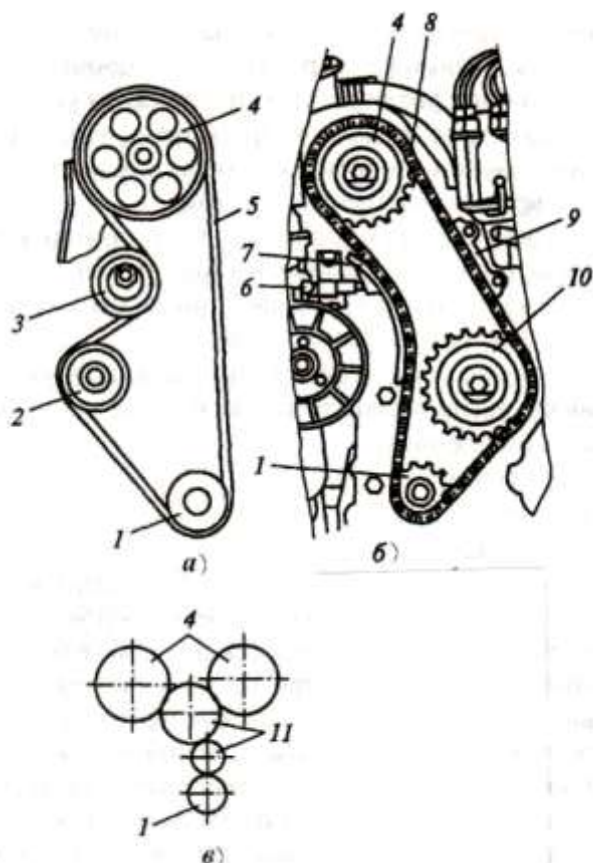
Различные способы привода распределительного вала: а — ремень; б — цепной; в — с зубчатым зацеплением: 1 — коленчатый вал; 2 — жидкостной насос; 3 — натяжной ролик; 4 — распределительный вал; 5 — приводной ремень; 6 — натяжитель цепи; 7 — башмак натяжителя цепи; 8 — цепь; 9 — успокоитель цепи; 10 — масляный насос; 11 — промежуточный вал
